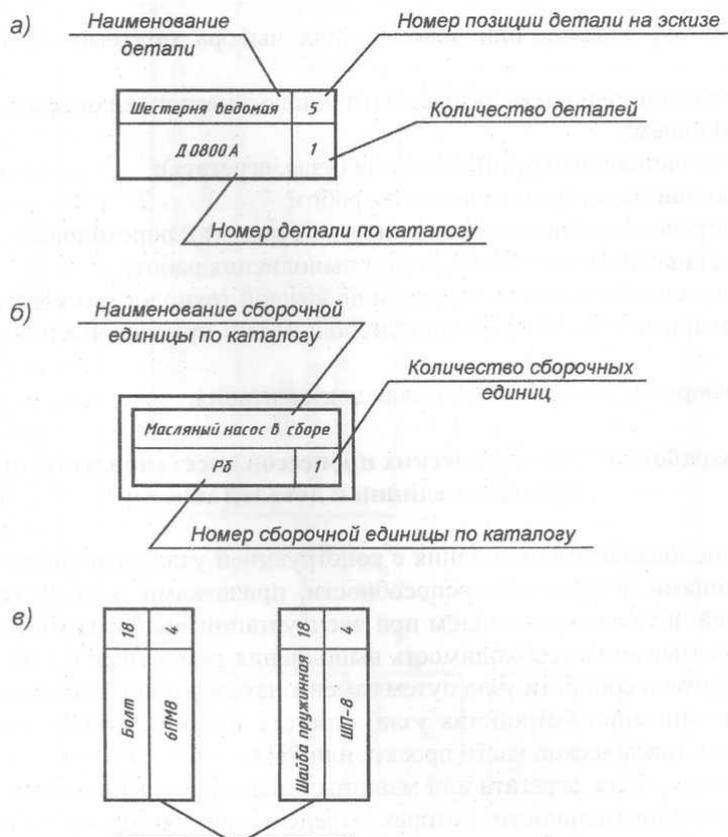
Условные обозначения на схеме разборки объекта: а - детали; б - разборочные группы; в - одновременное снятие двух деталей при разборке
